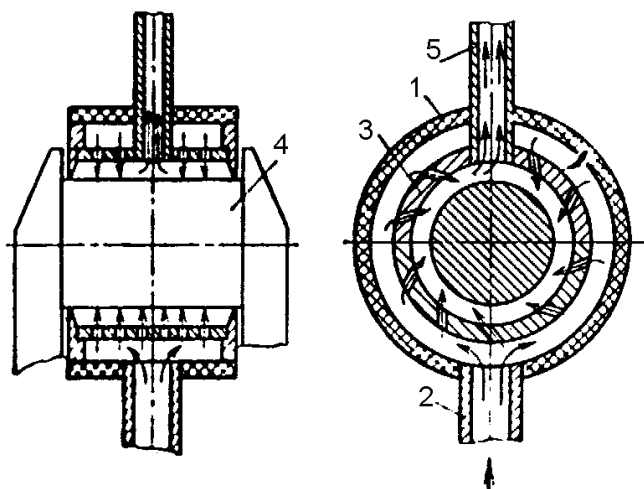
Схема ячейки для струйного электроосаждения металла на шейку вала: 1—корпус; 2—подводящий штуцер; 3—анод; 4—деталь; 5—отводящий штуцер
